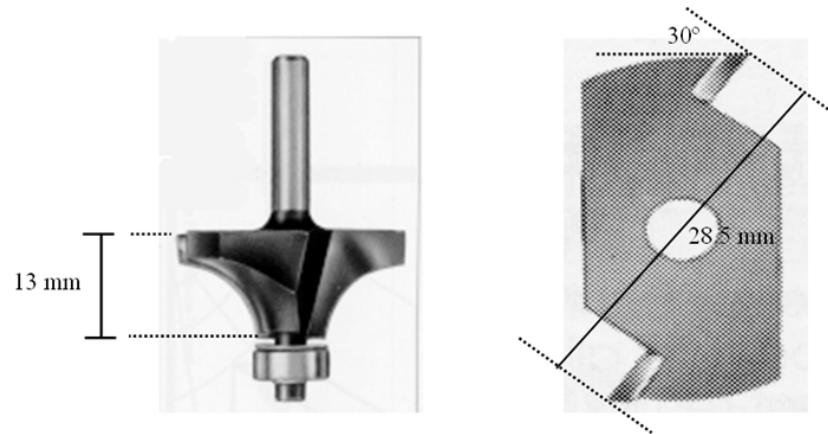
Broca con pastillas de carburo de tungsteno y con moldura.
